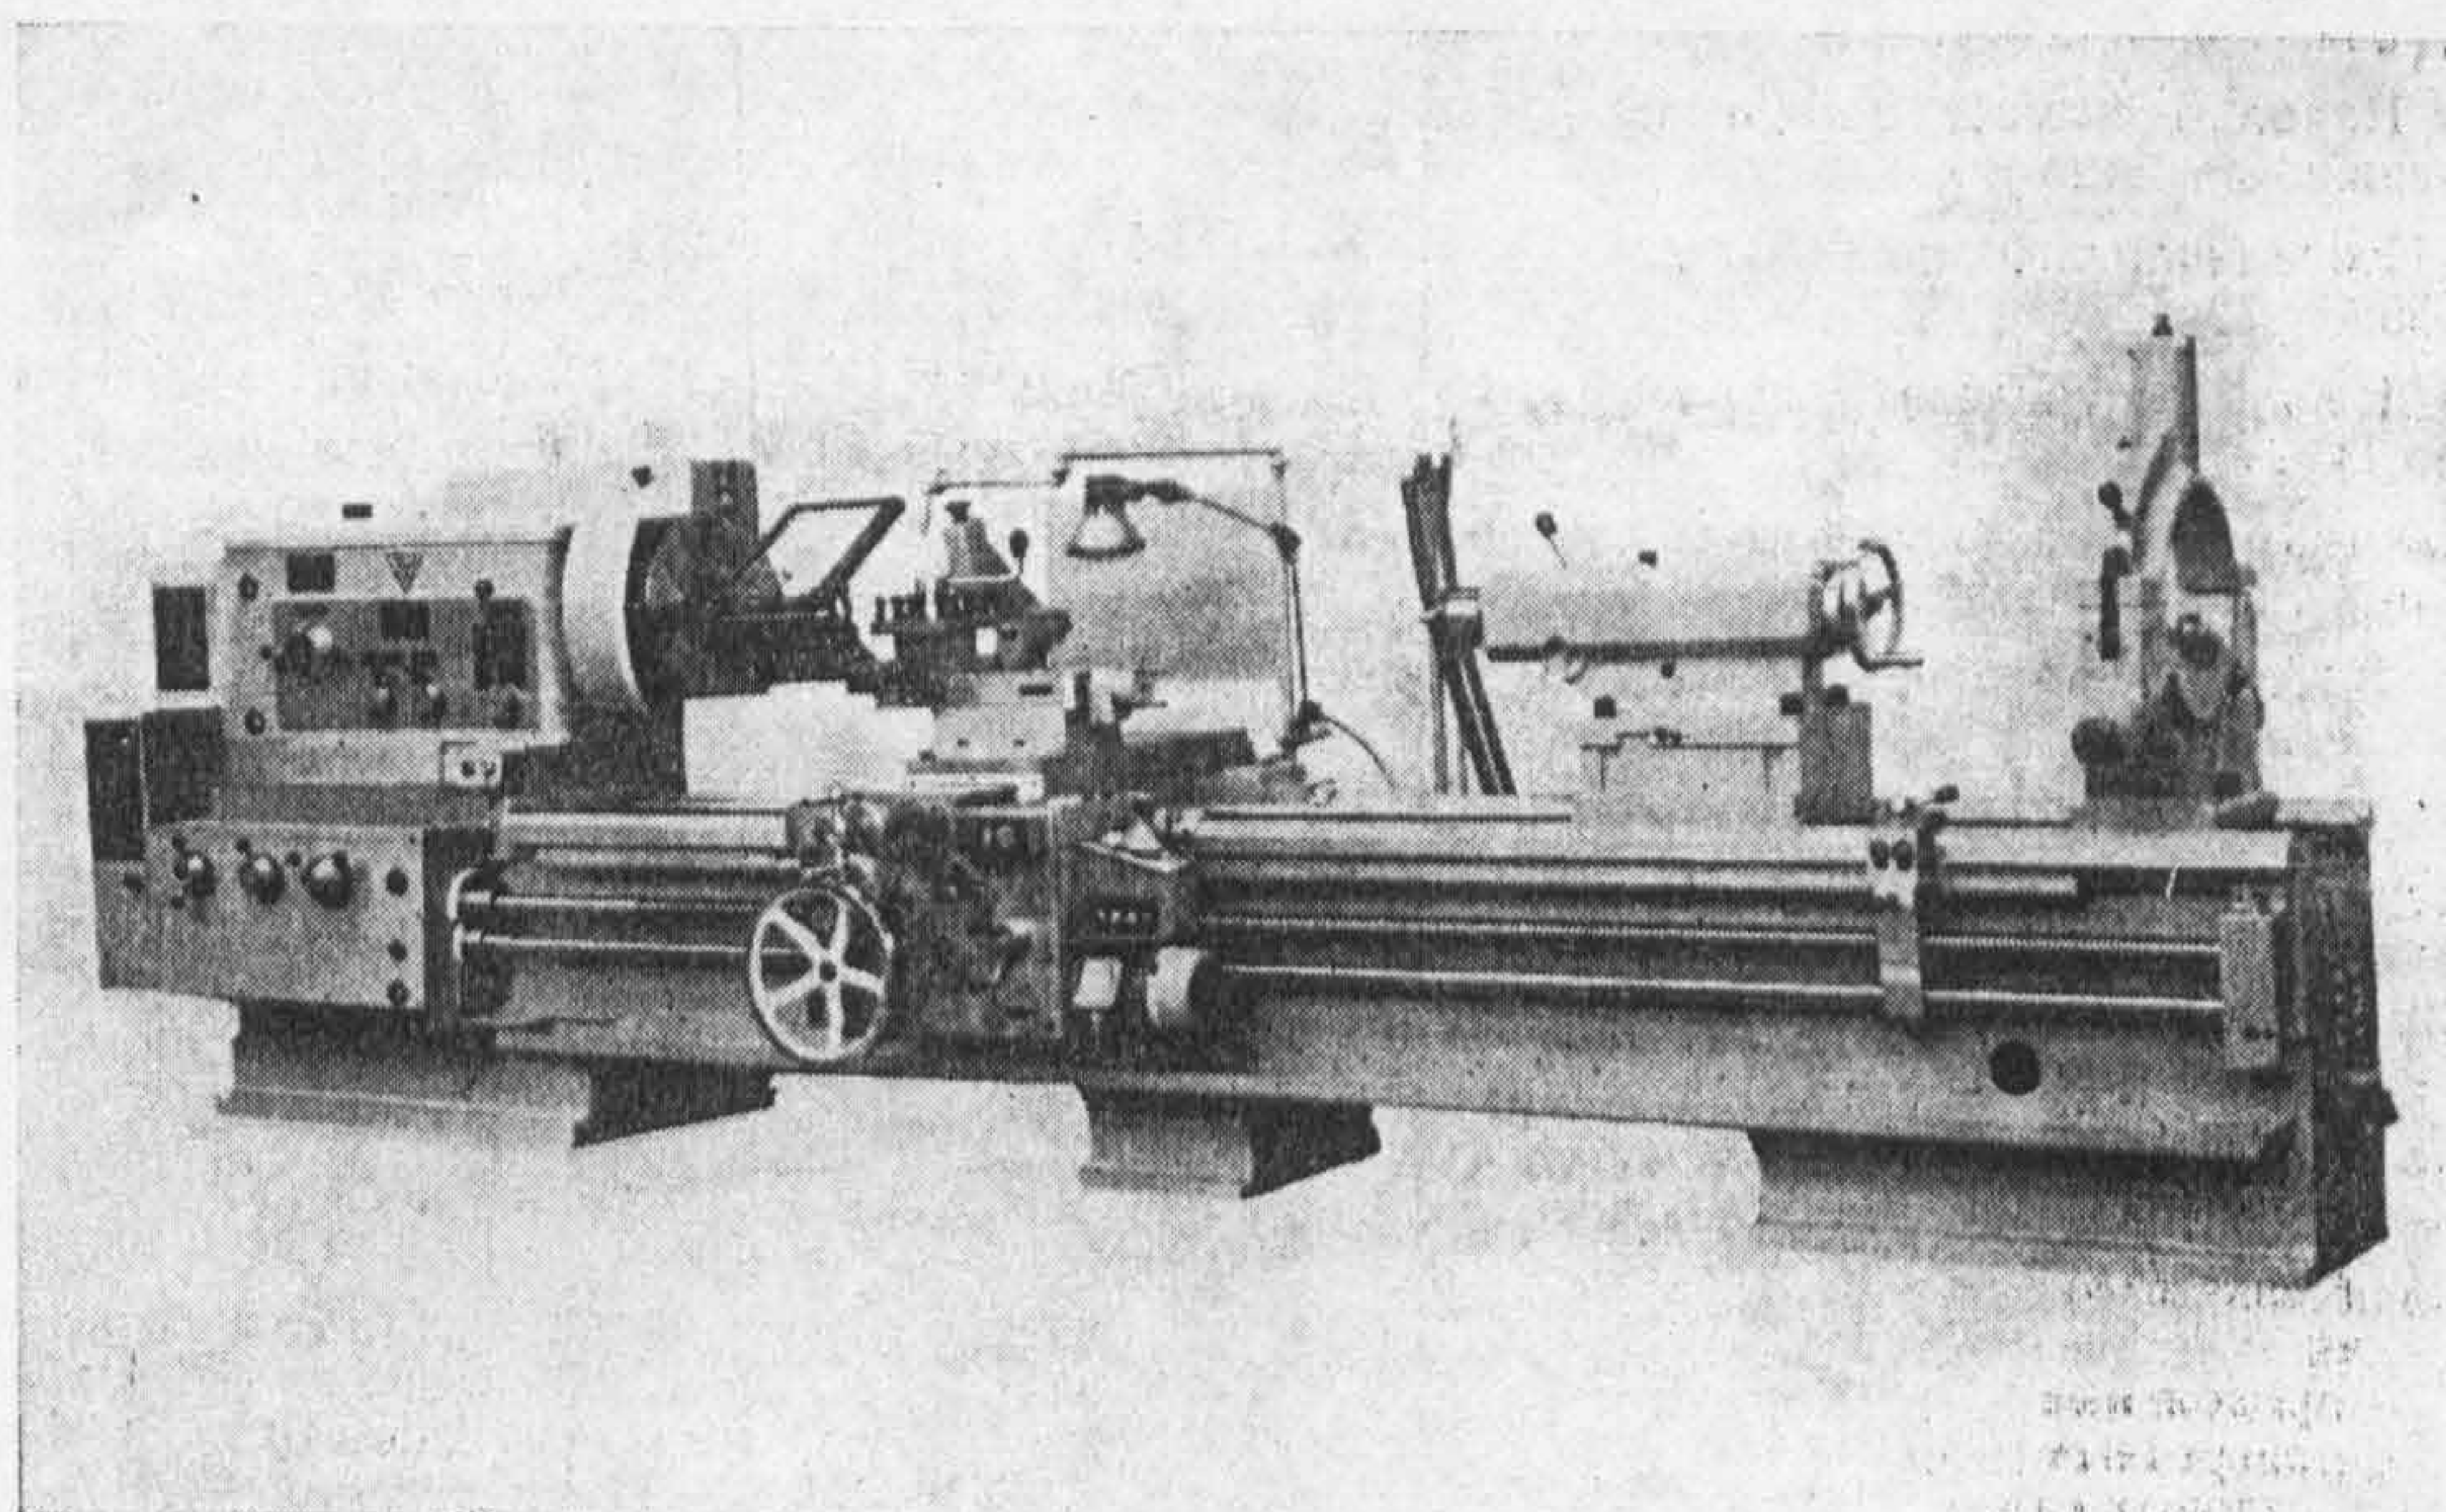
Общий вид токарно-винторезного станка мод. 16К40.
